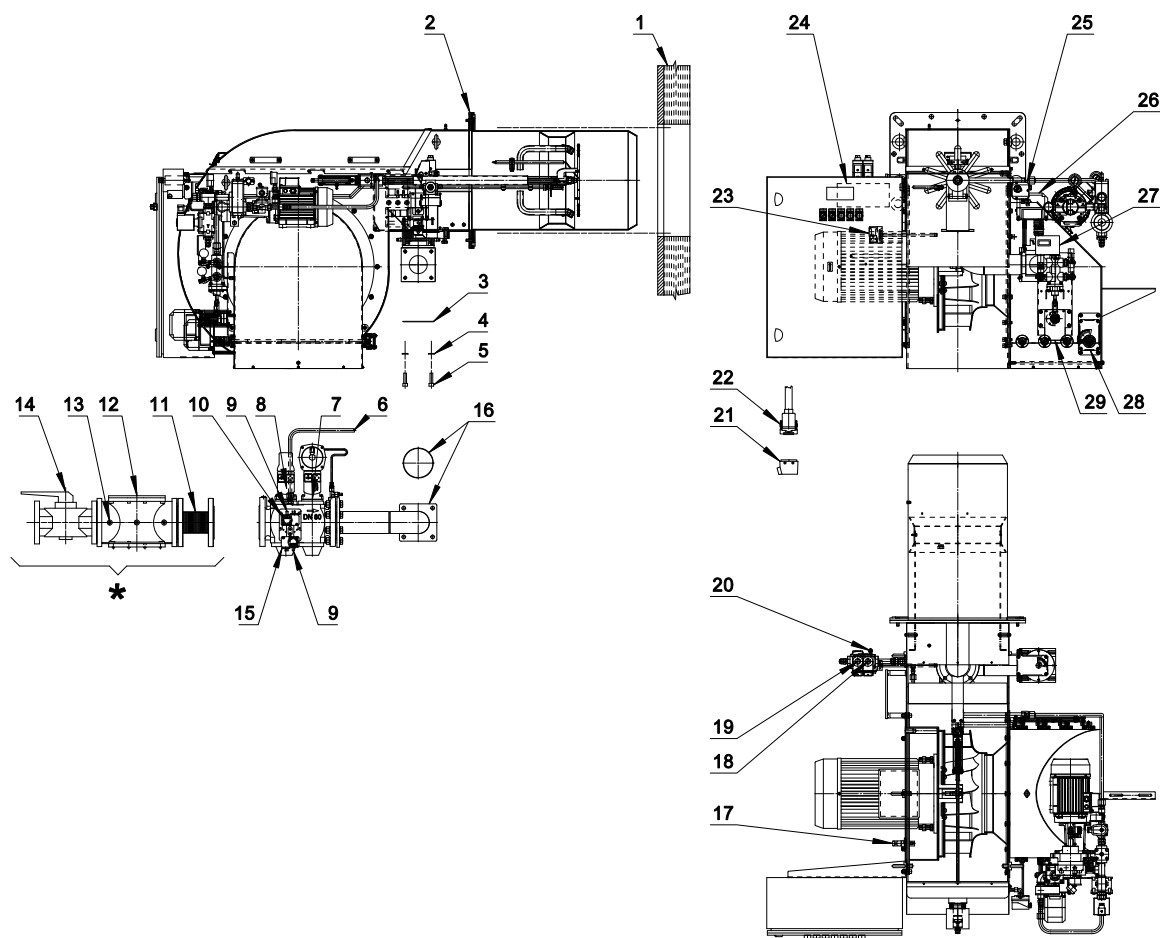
УСТАНОВКА ГОРЕЛКИ
